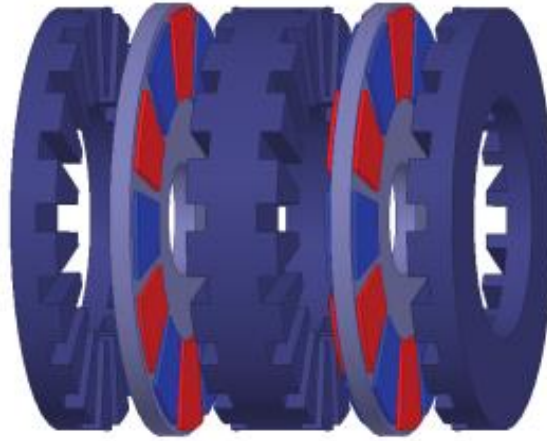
Machine à flux axial « multi-étages » à rotor interne [20]
